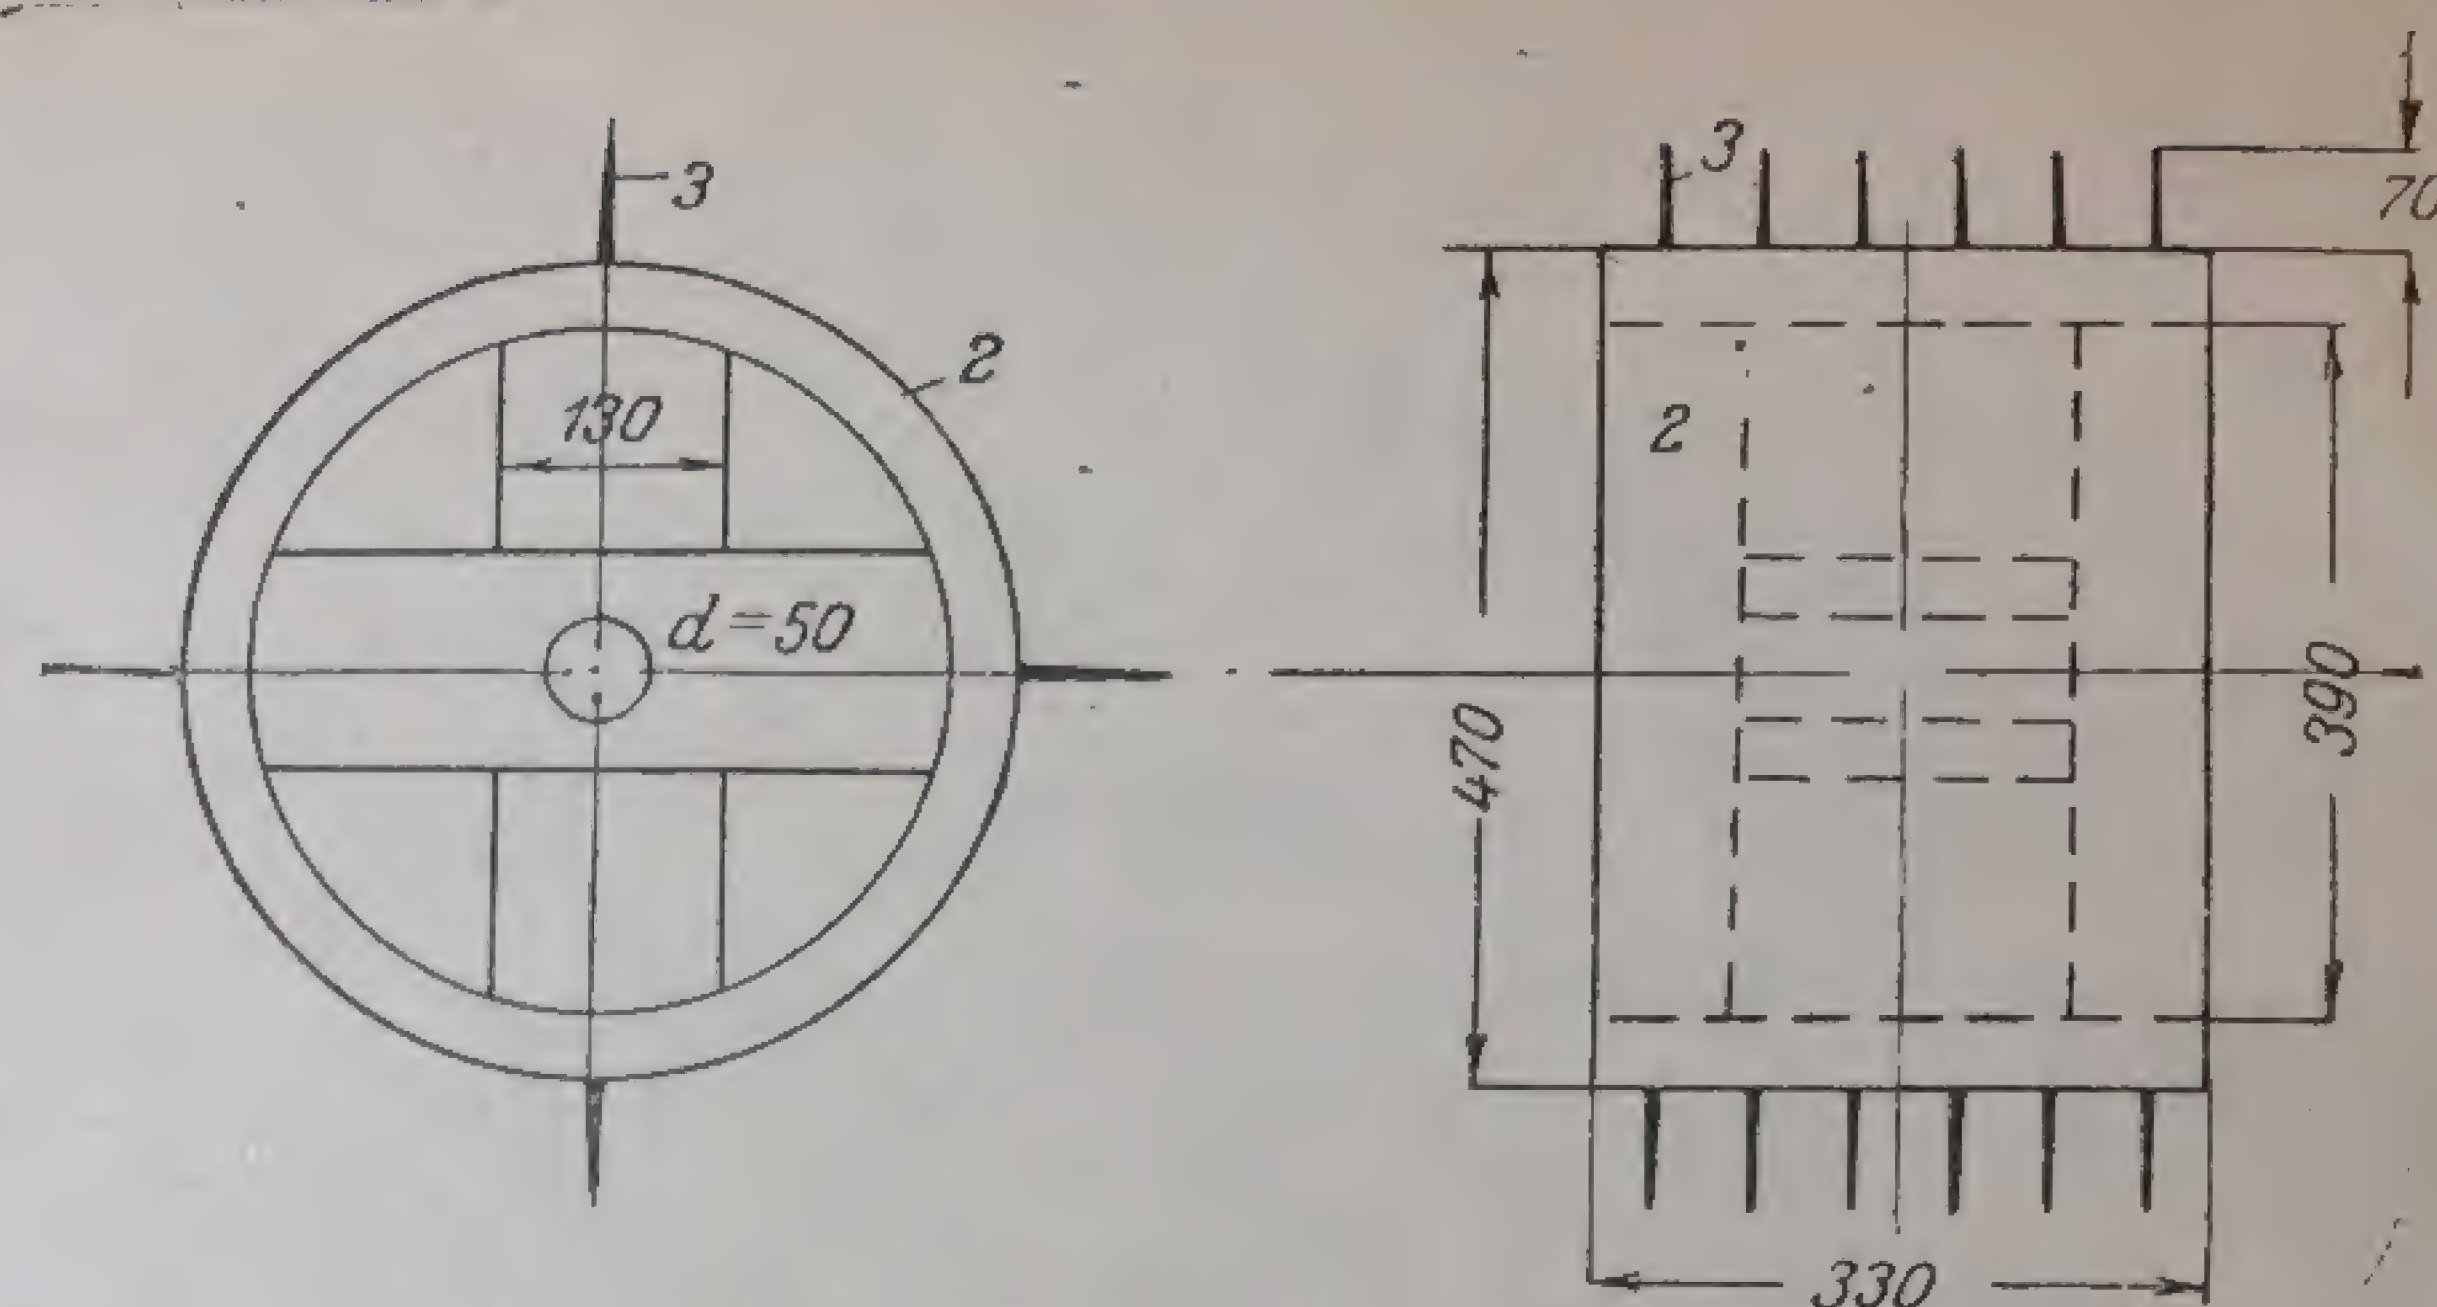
Приспособление для очесывания тресты перед мятьем:
